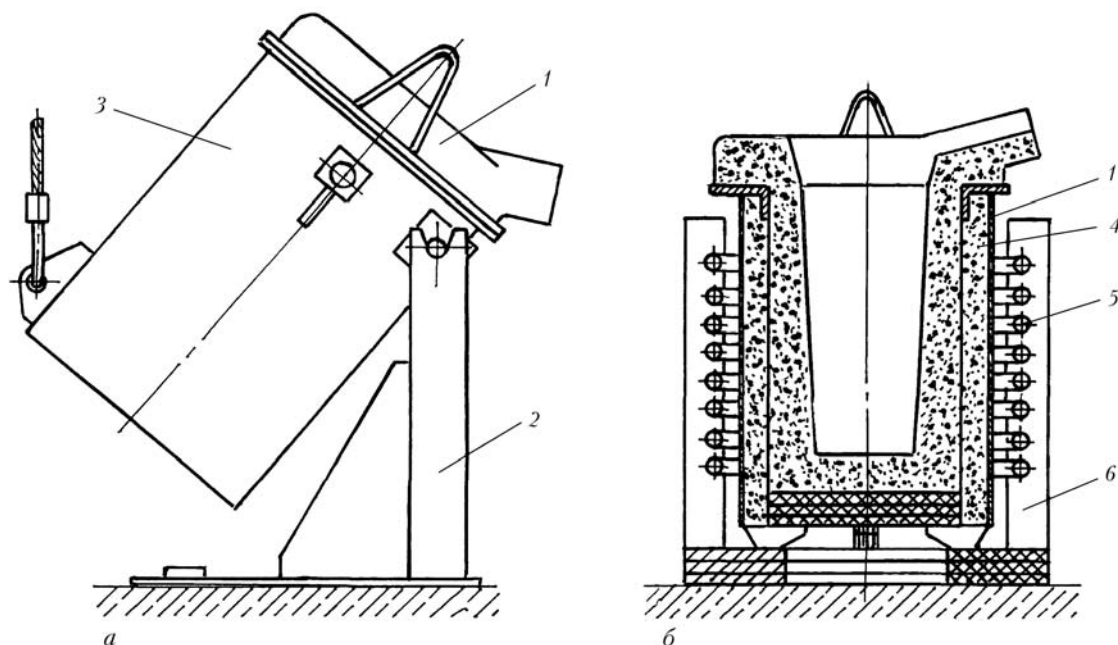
Схема лабораторного плавильно-разливочного модуля (а) с индукционным нагревом металла в ковше-печи (б): 1 — ковш; 2 — механизм наклона; 3 — «стакан»; 4 — футеровка; 5 — индуктор; 6 — стойки для крепления индуктора
